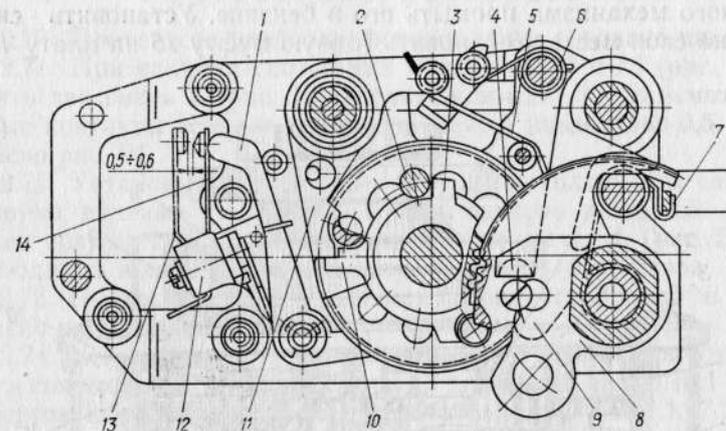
Положение зубчатых колес первой и второй шторок при взводе механизма выдержек:
